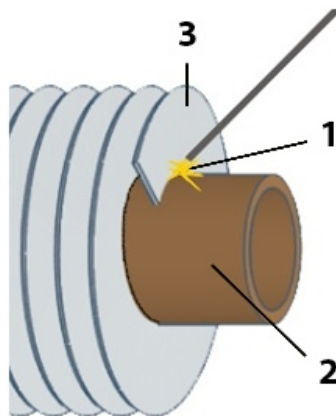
Общая схема оребрения сваркой: 1 – место подачи тока, 2 – несущая труба, 3 - ребро
